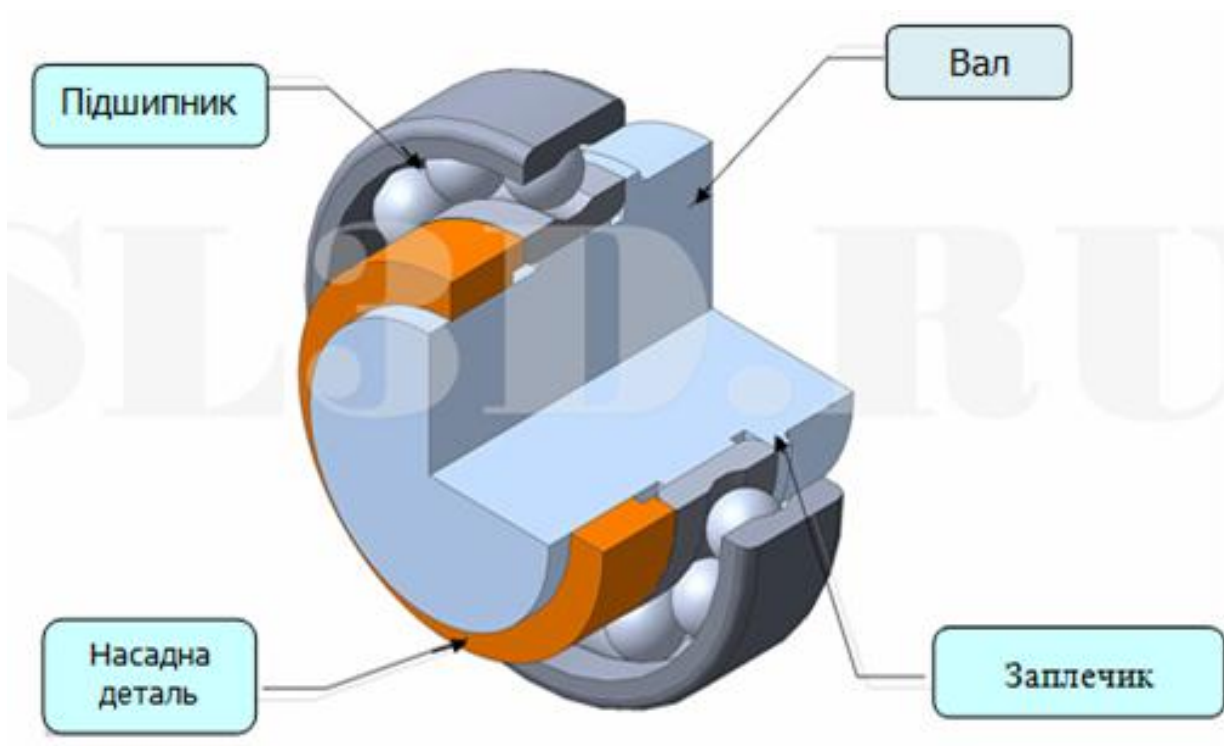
3. Установка підшипника з затягуванням через насадну деталь
